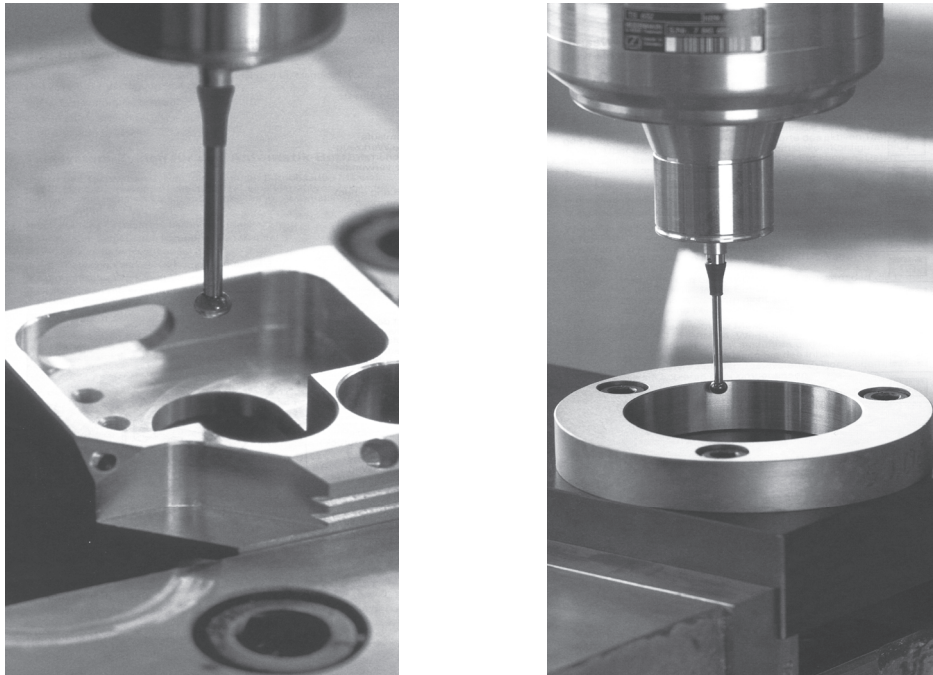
Активный контроль геометрических параметров заготовки щуповой головкой
